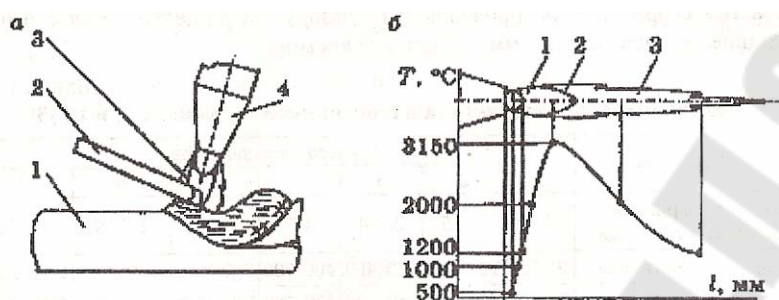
Схемы процесса газовой сварки (а) и ацетиленоxygenного пламени (б)
